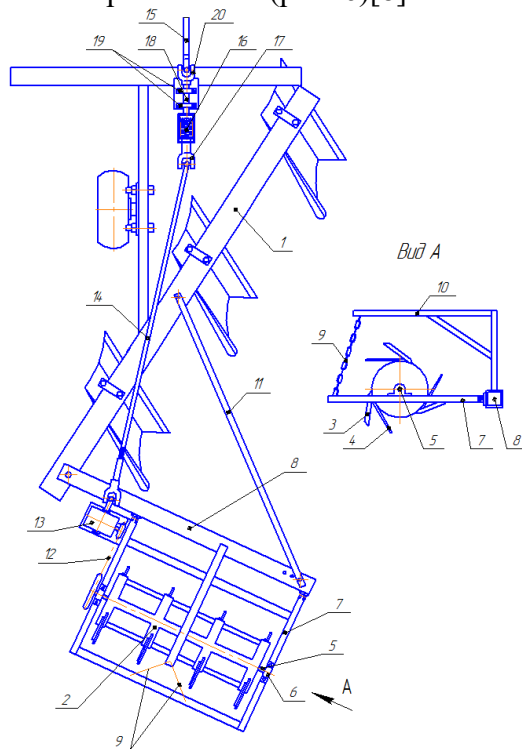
Конструктивно-технологическая схема пахотно-фрезерного агрегата
